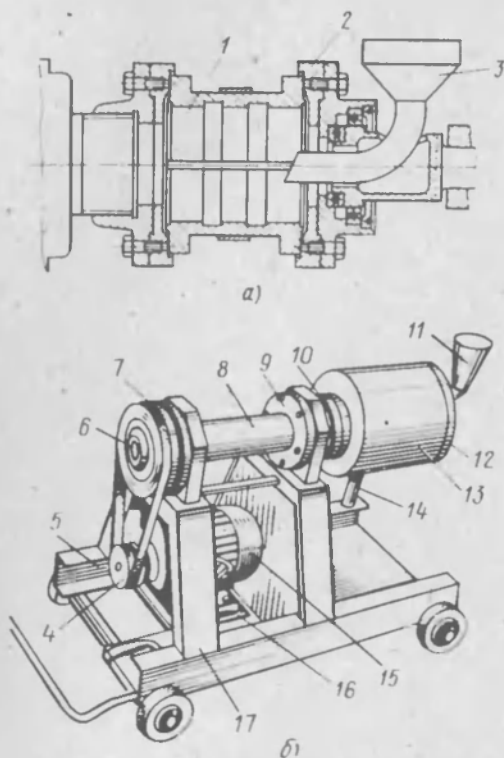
Центробежная заливка подшипников скольжения в приспособлении к токарному станку (а) и переносном станке (б)
